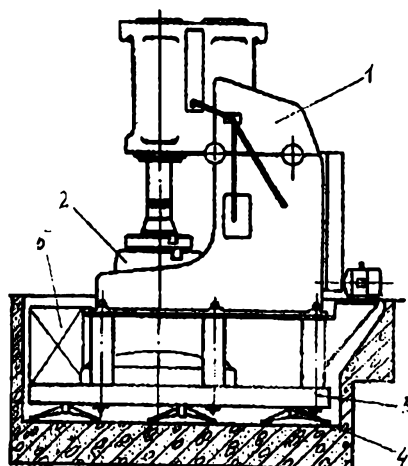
Виброизолирующая установка пневматического ковочного молота:
